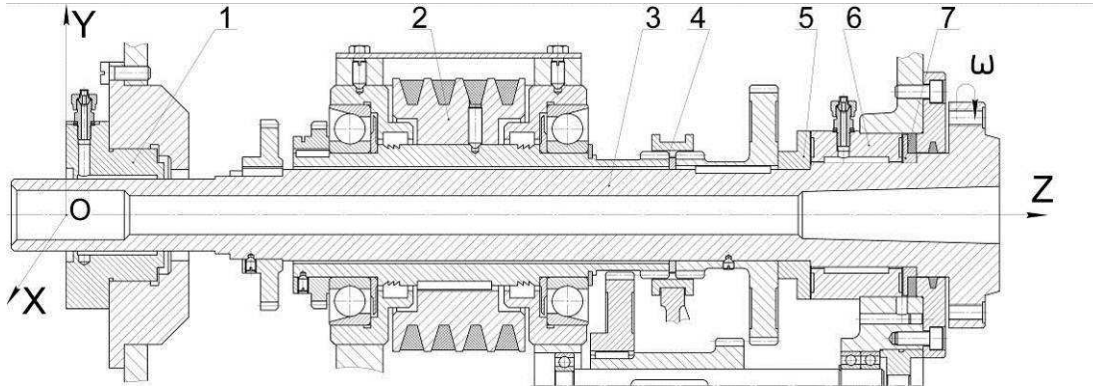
Конструктивна схема шпиндельного вузла токарного верстата УТ16А:
